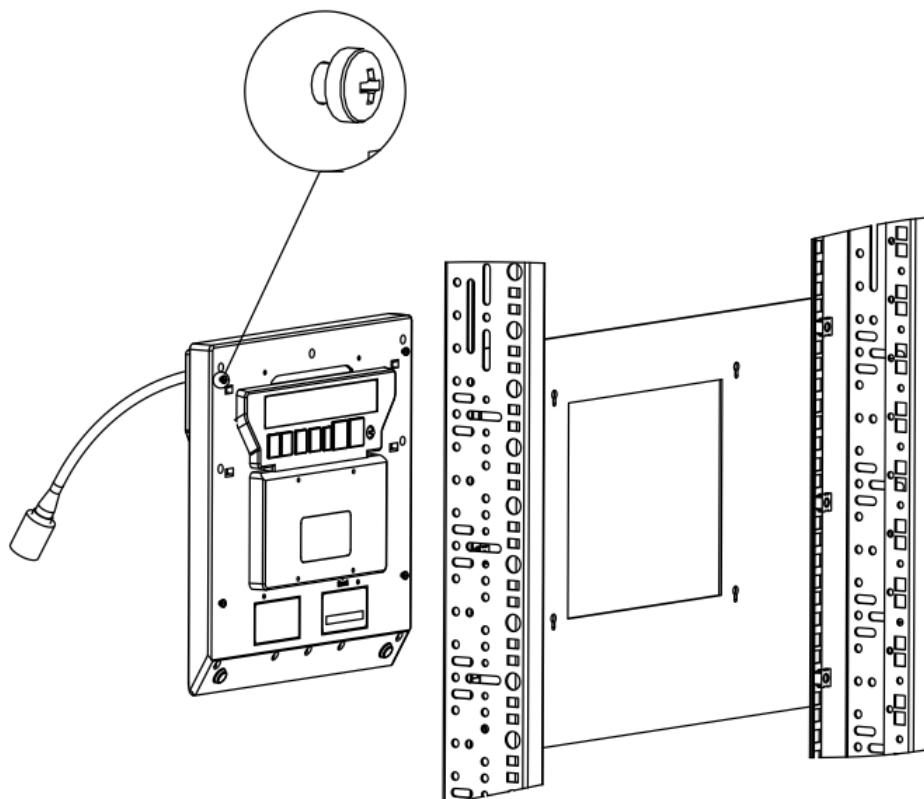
Установка TOP-PAD-IP2 на панель 7U
